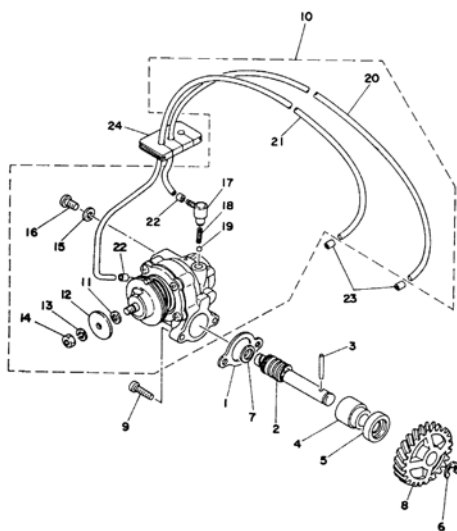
Die Ölpumpe wird von zwei Schrauben gehalten. Auf der Welle befindet sich zwischen Pumpe und Motorgehäuse eine Bz-Scheibe
